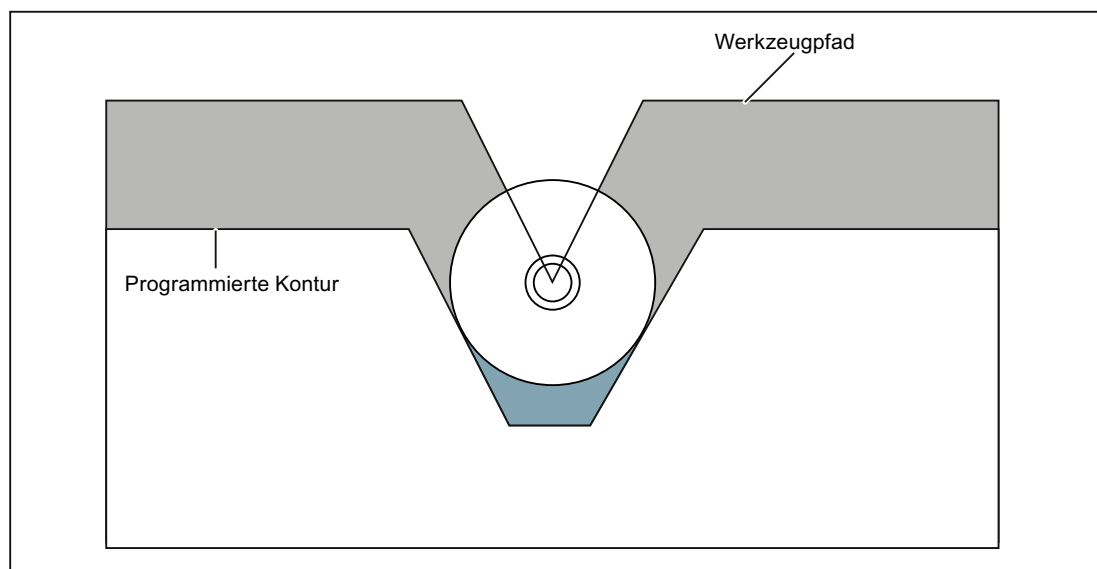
Werkzeugradius zu groß für die Innenbearbeitung
